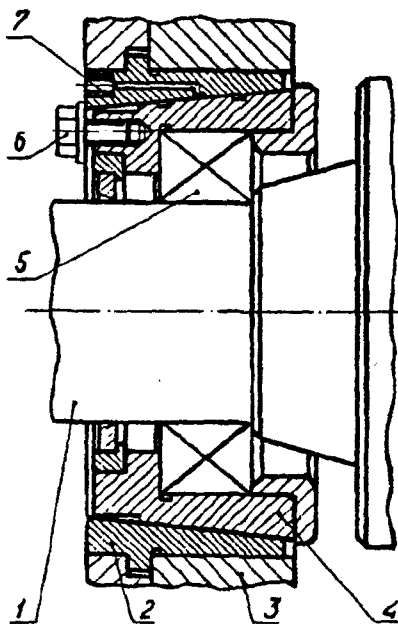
Устройство для регулировки зазора в подшипнике качения
